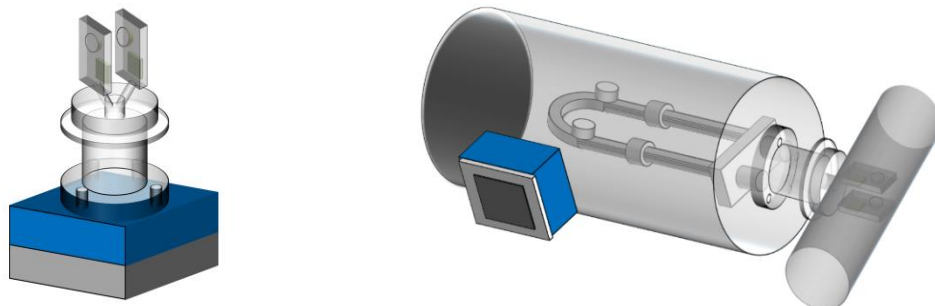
Esquema Sonatec TR (esquerda, Adaptado de [27]) / Combitec (direita, Adaptado de [28])
